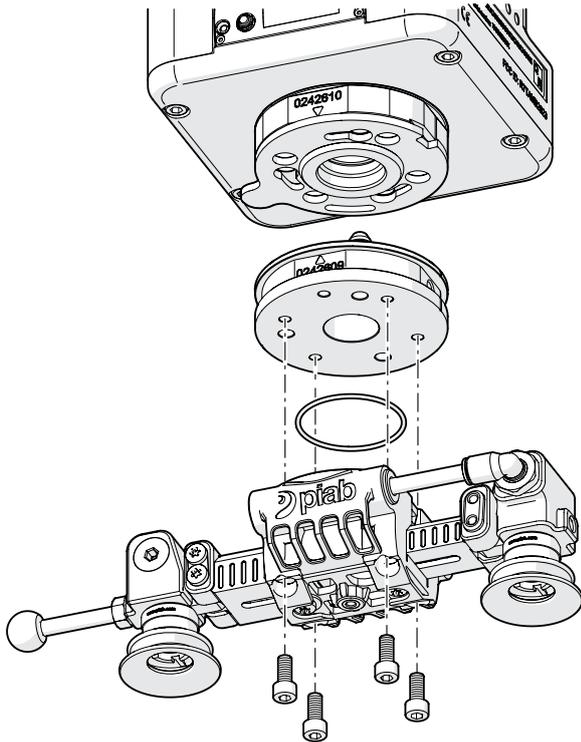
Der einstellbare Greifer wird über den Werkzeugwechsler am piCOBOT® Electric befestigt.
